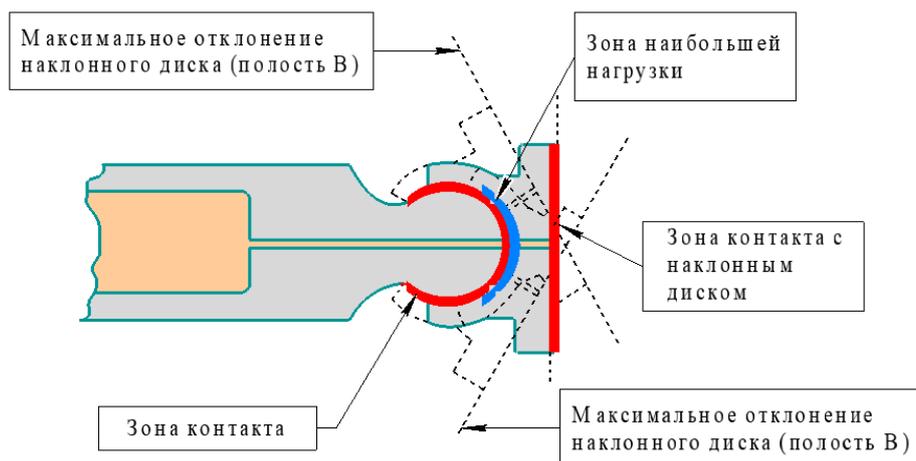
Схематичное расположение областей наибольшей нагрузки гидростатического башмака
